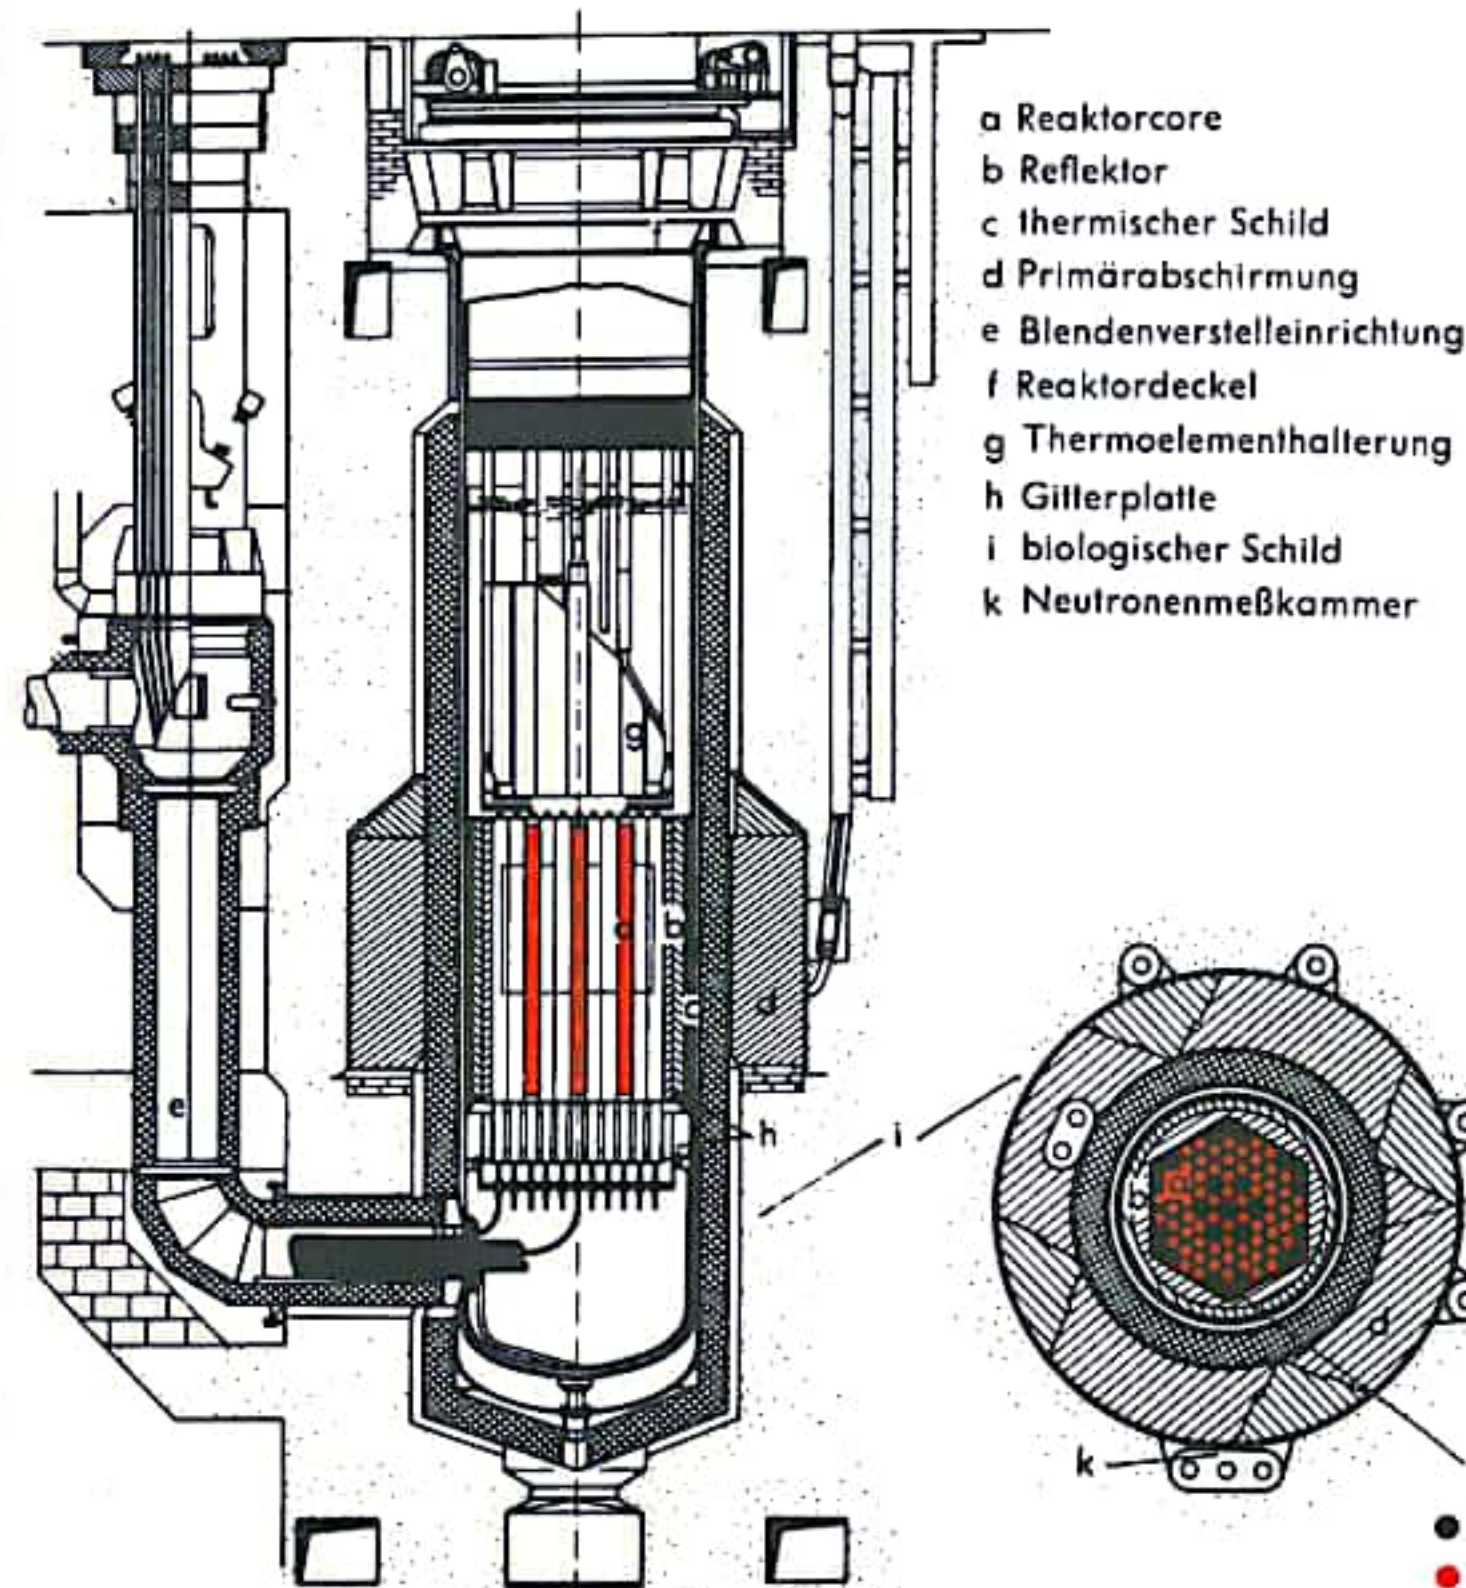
KNK-Reaktor (Längs- und Querschnitt)
